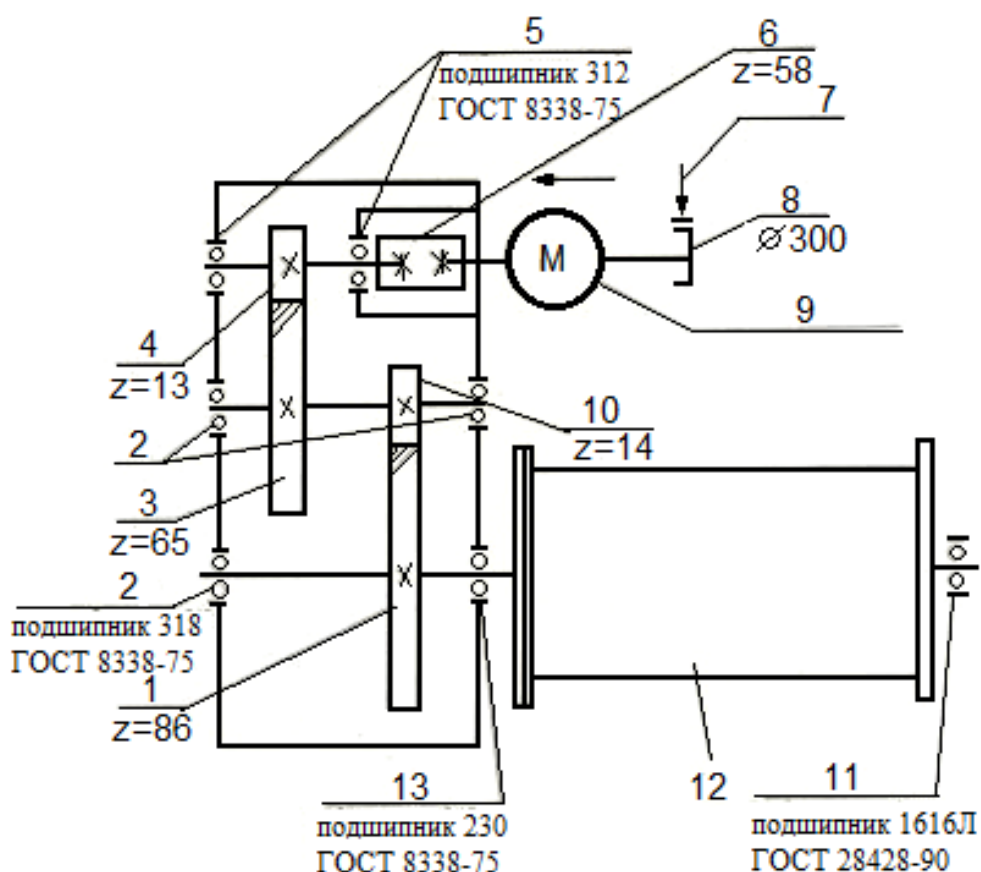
Схема кинематическая грузовой лебедки
